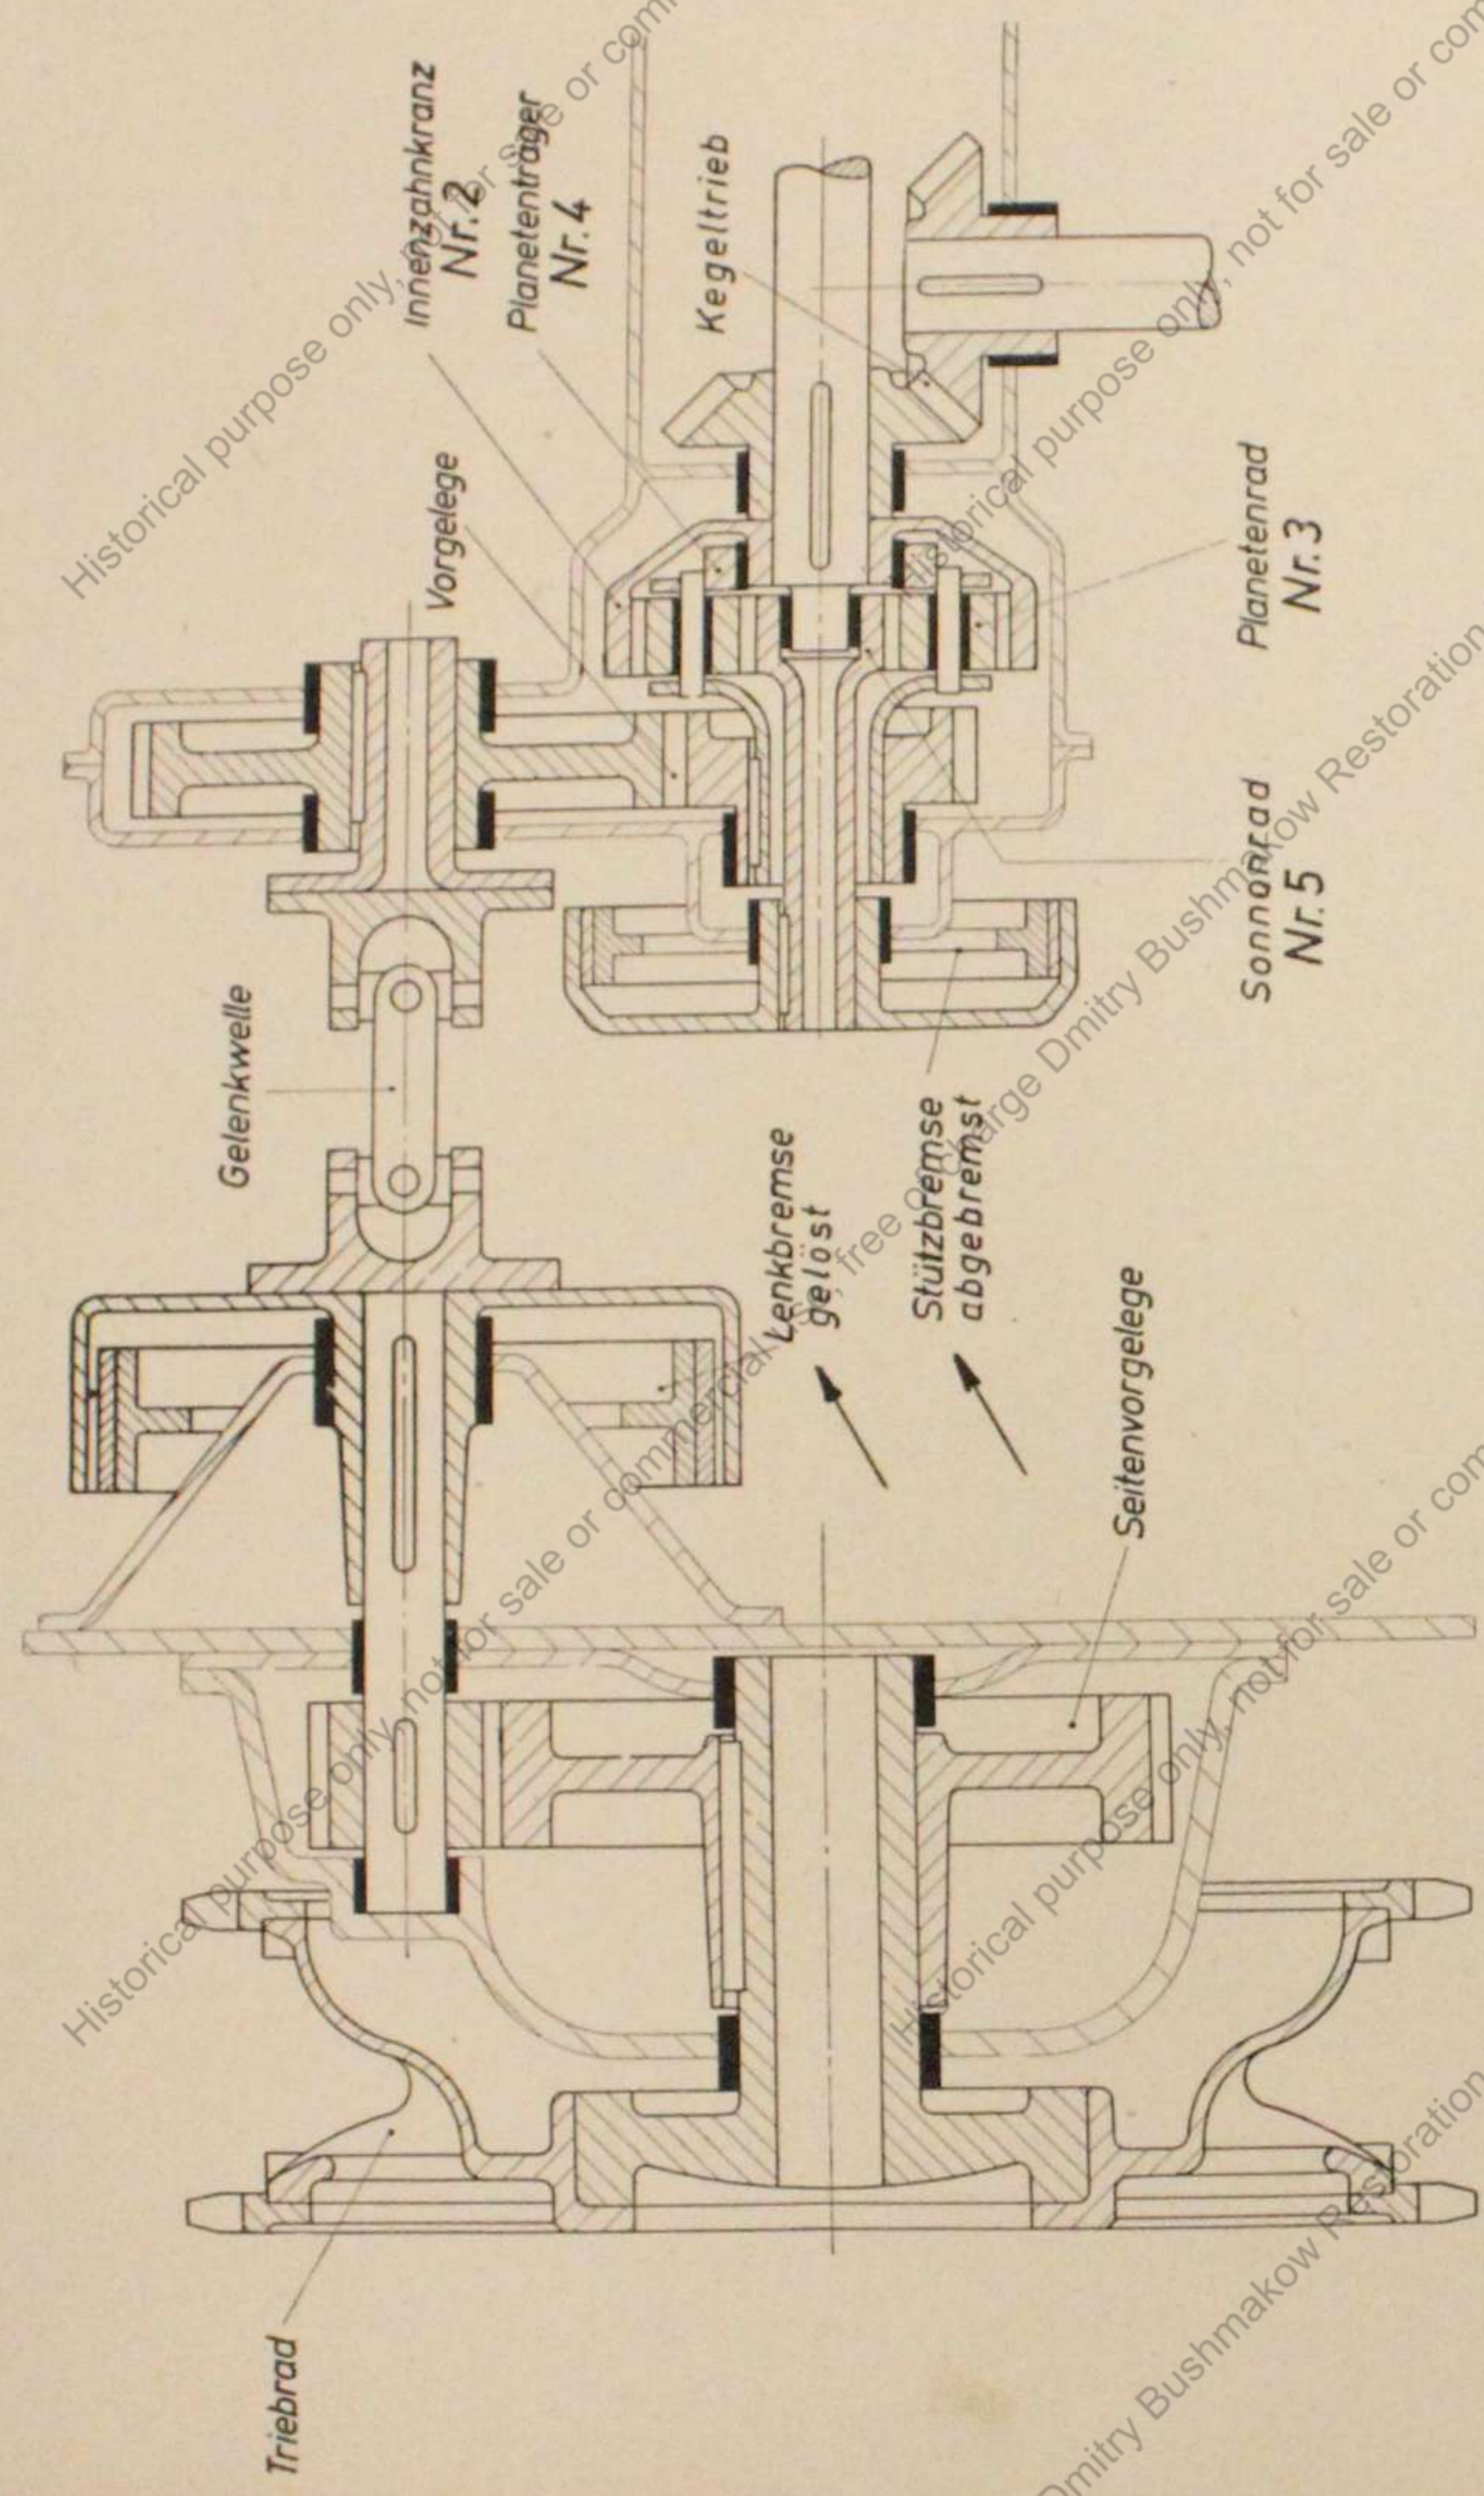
Lenkgetriebe, Plan (Geradeausfahrt)
